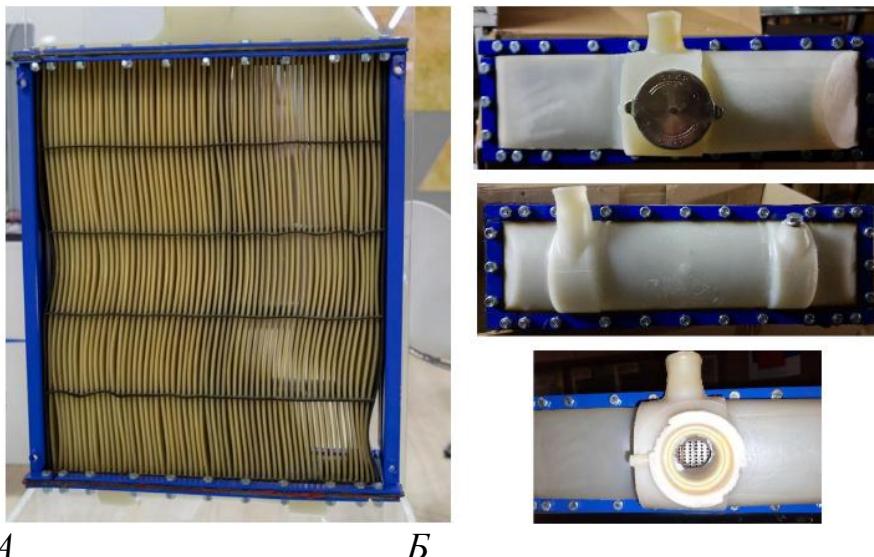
Радиатор системы охлаждения с полиуретановой сердцевиной для двигателя: А - общий вид сердцевины радиатора; Б - вид сверху, снизу и внутренней части верхнего бачка радиатора
